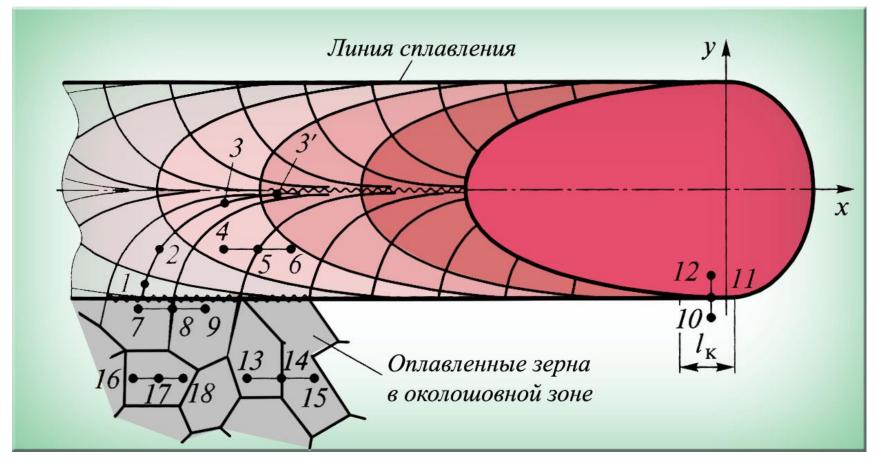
Виды МХН в сварном шве (отрезки – базы определения МХН; I_К – участок контакта расплавленного металла сварочной ванны с основным металлом)
